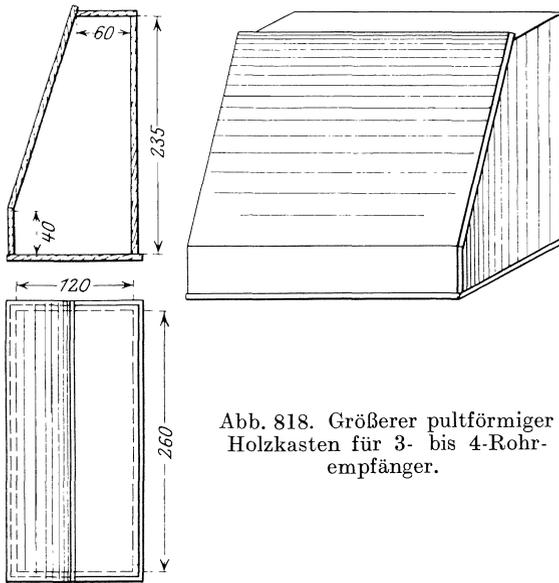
Größerer pultförmiger Holzkasten für 3- bis 4-Rohrempfänger.
